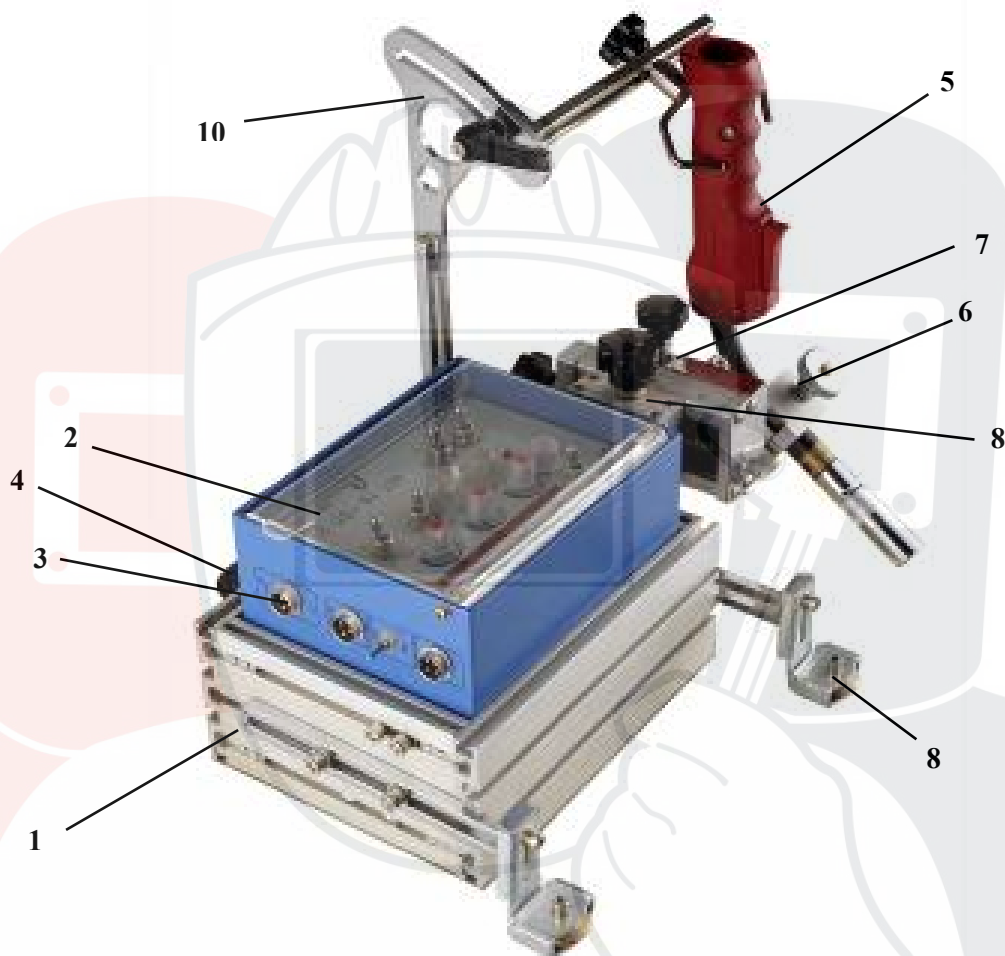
Сварочная каретка HIT-18-1SD-2 – внешний вид
